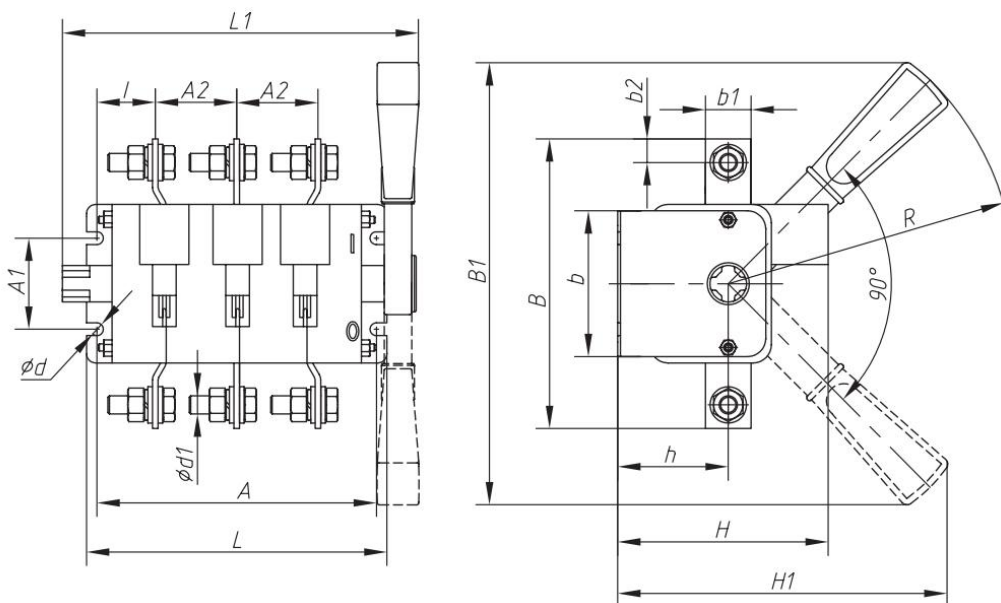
Выключатель-разъединитель универсальный трехполюсный на одно направление с д/г камерами, несъемная левая/правая рукоятка
